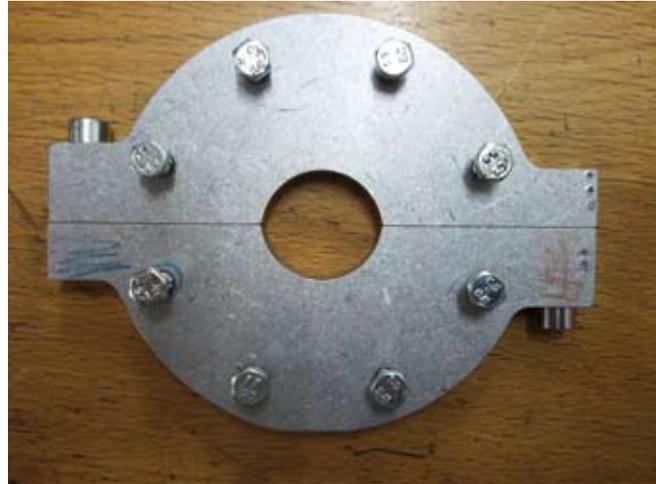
Rückseite des Flansches mit seitlich angebrachten Senkkopfschrauben
